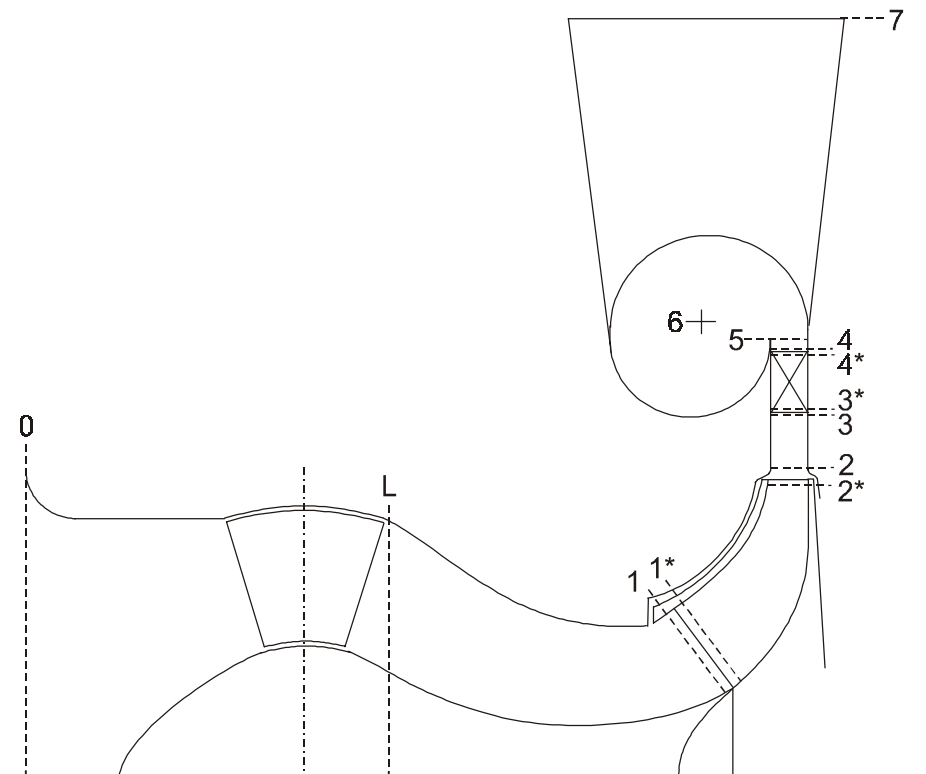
Schnittbild eines Radialverdichters mit Kontrollebenen
